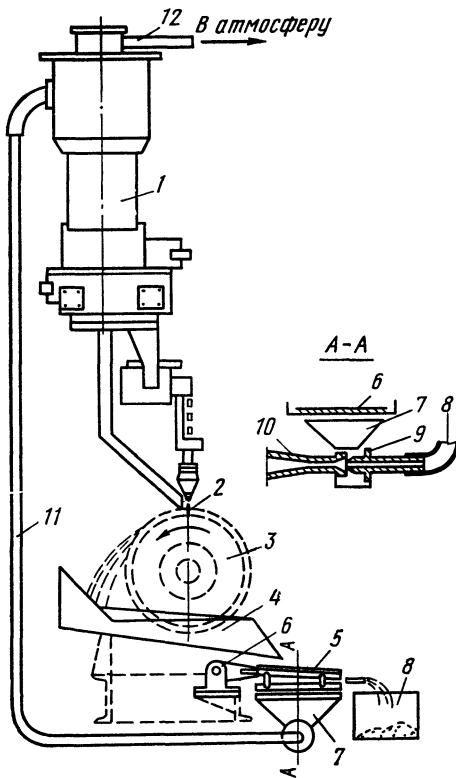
Схема пневматической подачи флюса в бункер наплавочной установки
